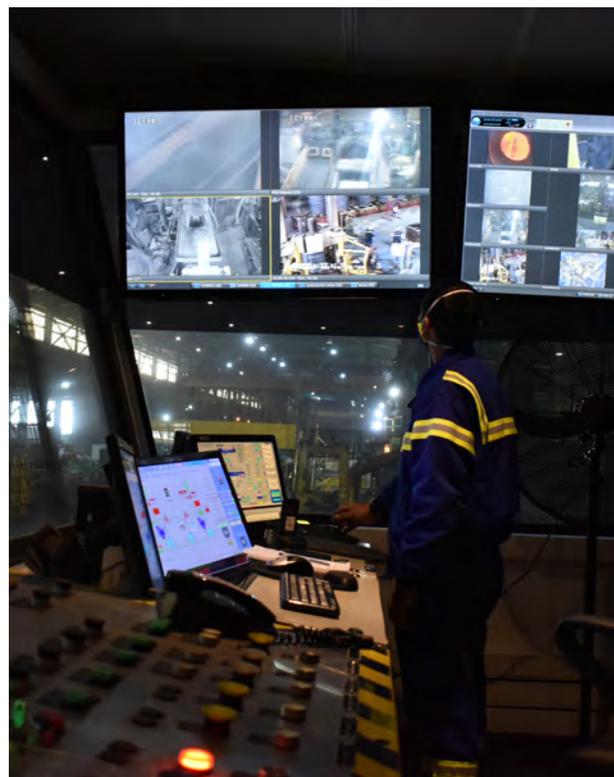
Sala de Control de Laminación, Planta Colina, AZA.
